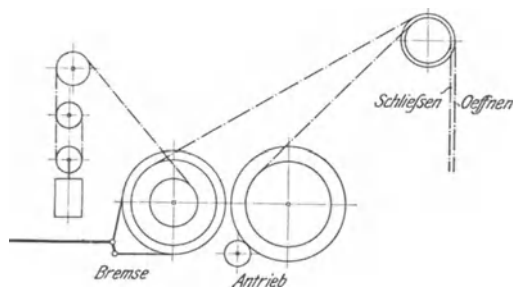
Greiferwinde mit Gegengewichtsantrieb für die Entleertrommel.
